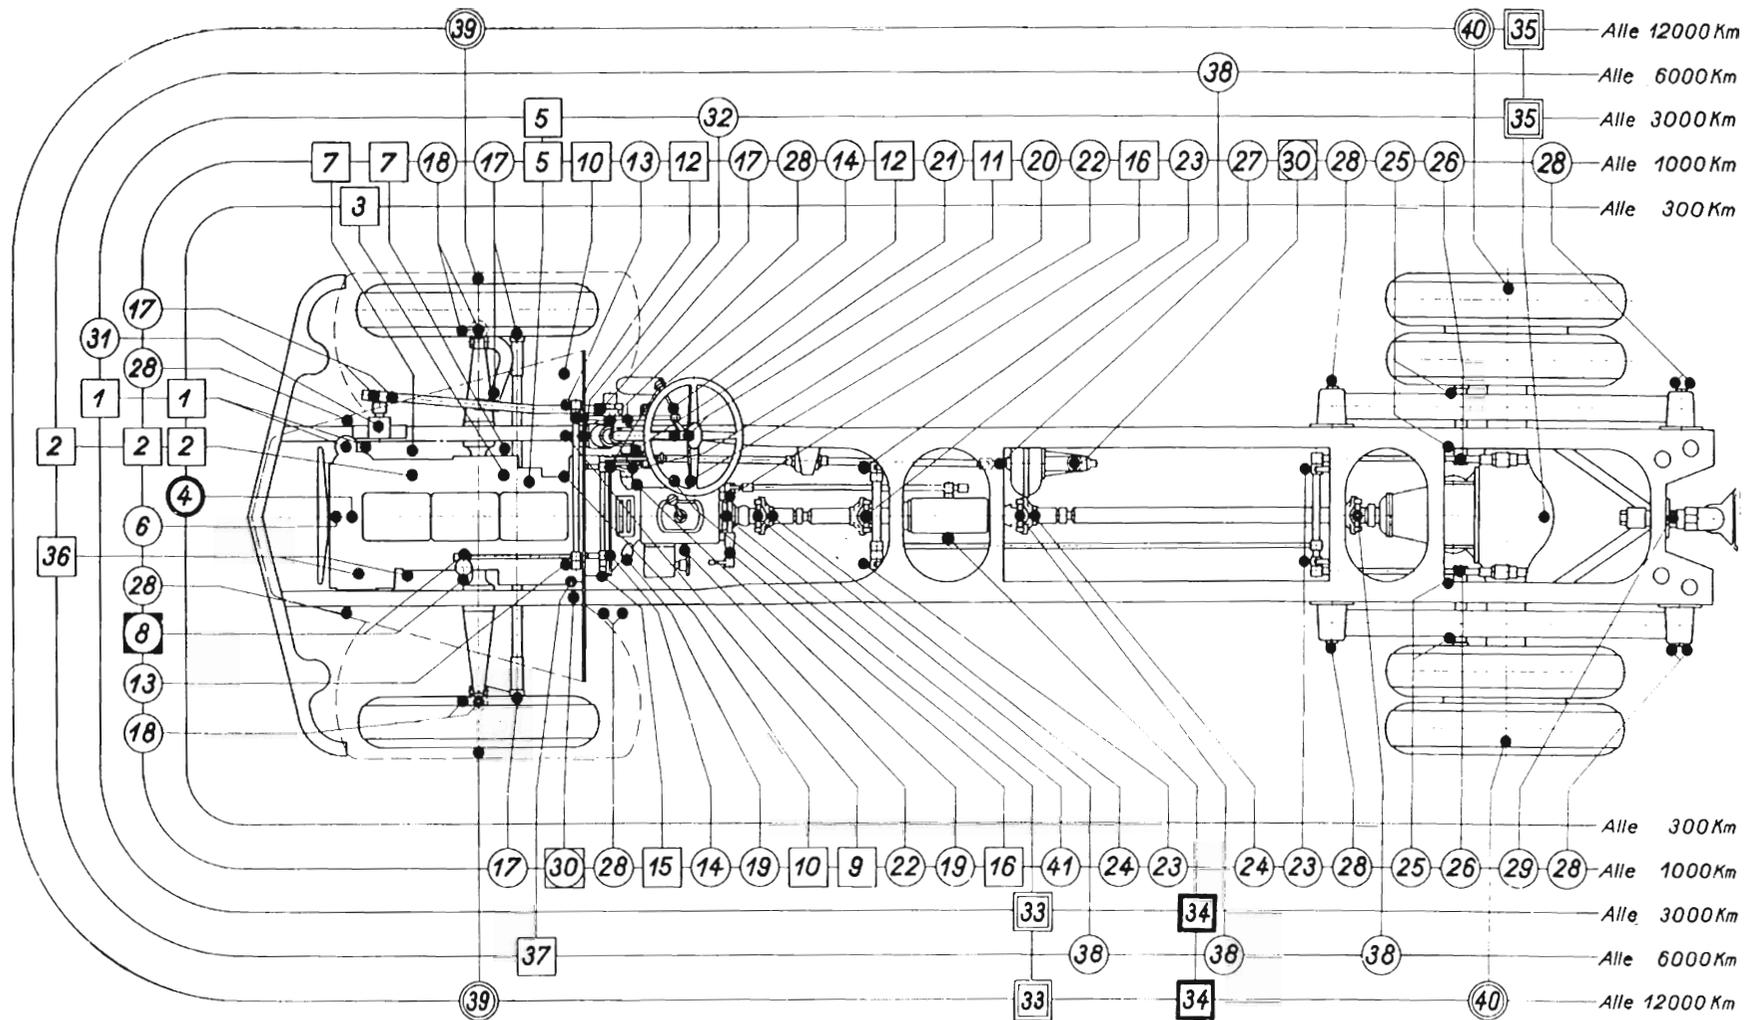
Schmierplan zu DD-Motor und Chassis Type AS 47
